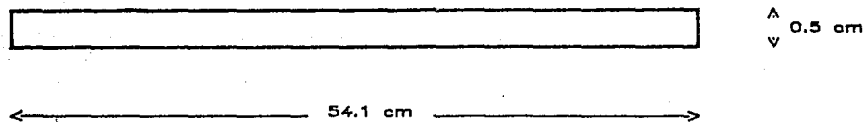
ARISTA DE LA LAMINA EXTERIOR
